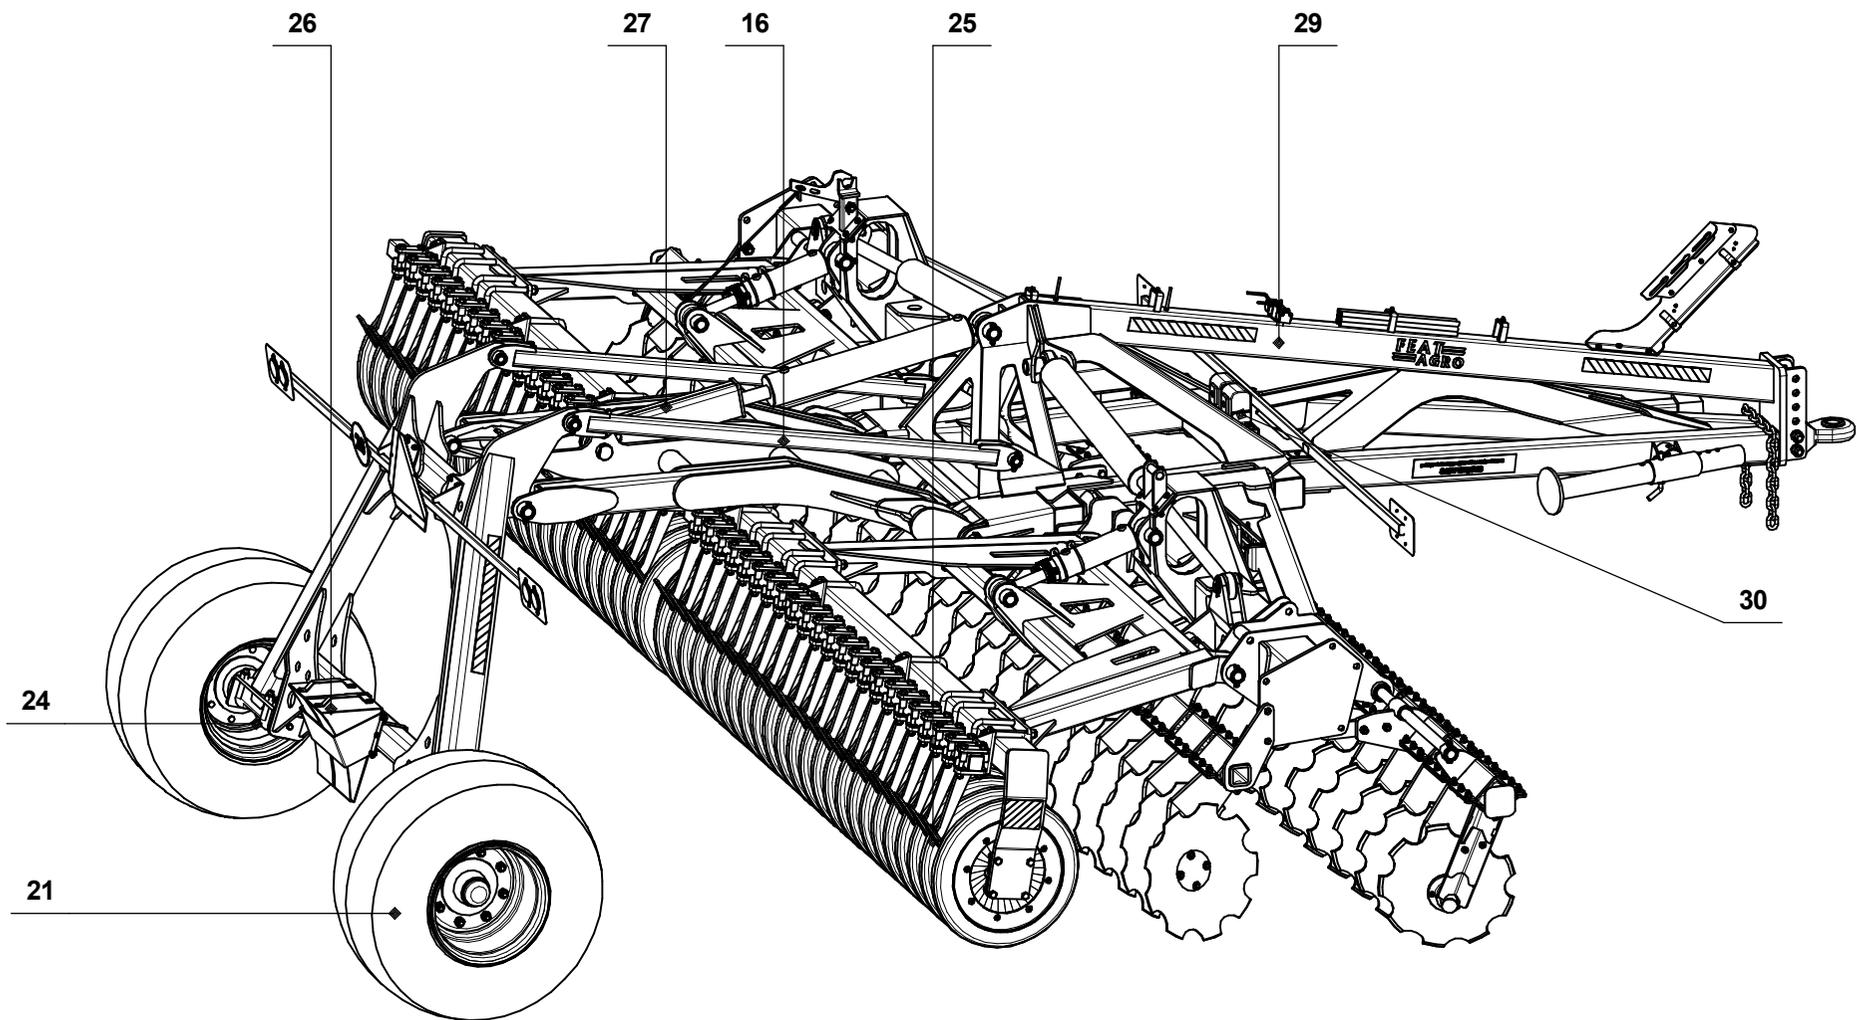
Общий вид дисковой почвообрабатывающей машины ДПМ «Универсал» / «Универсал Т»
